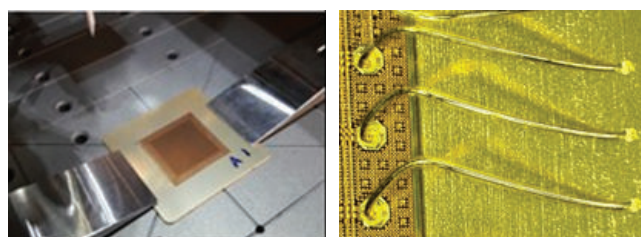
образец со сварными соединениями из золотой проволоки, созданными с помощью установки F&S Bondtec. Слева показано расположение образца на рабочем столе установки, справа – петли сварных соединений.
